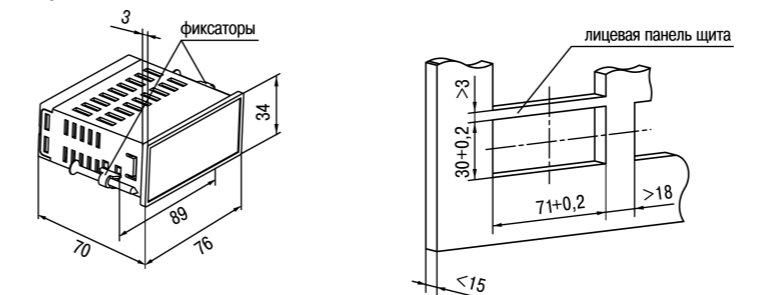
Габаритные размеры корпуса ЩЗ
